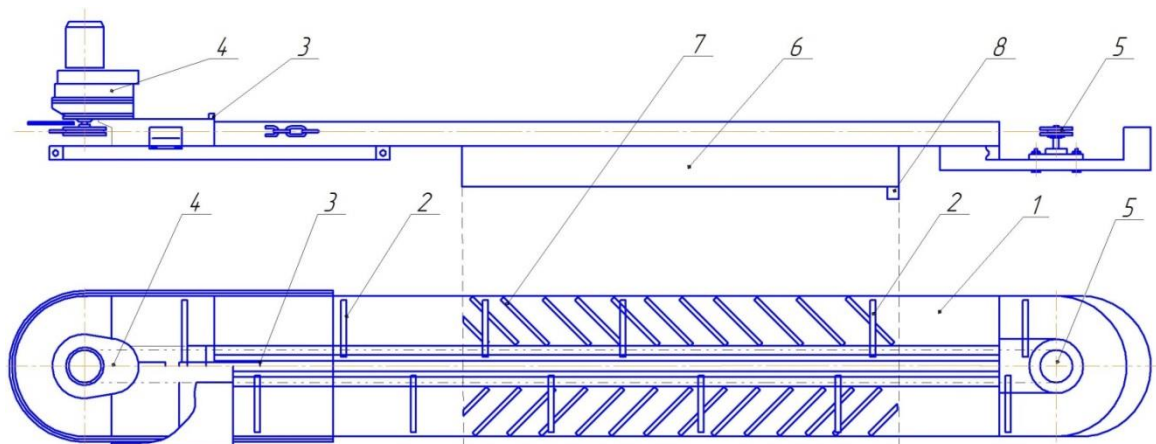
Загальний вигляд транспортера: 1 – короб, 2 – ланцюгово-скребковий транспортер, 3 – натяжний пристрій, 4 – приводна станція, 5 – поворотна зірочка, 6 – лотік, 7 – вирізані щілини у днищі жолоба, 8 – патрубок.
